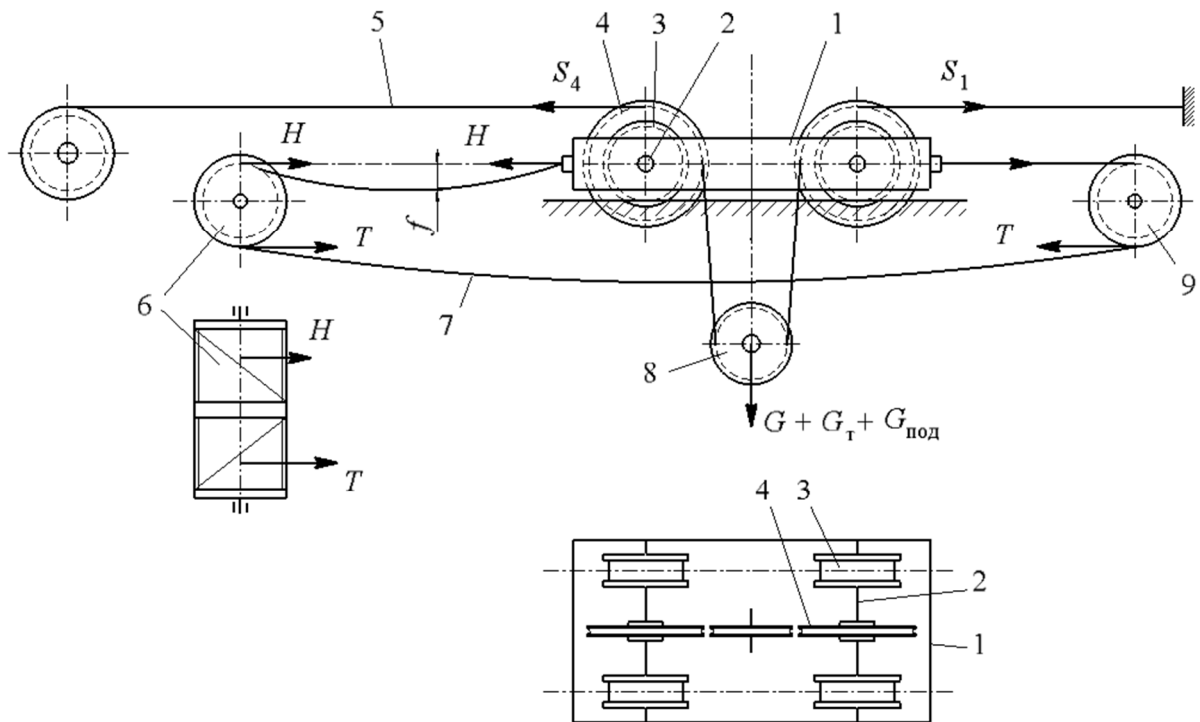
Схема механизма передвижения тележки с канатной тягой: 1 — рама тележки; 2 — ось блоков и ходовых колес; 3 — ходовое колесо; 4 — блок механизма подъема; 5 — подъемный канат; 6 — барабан механизма передвижения; 7 — тяговый канат; 8 — блок подвески; 9 — обводной блок
